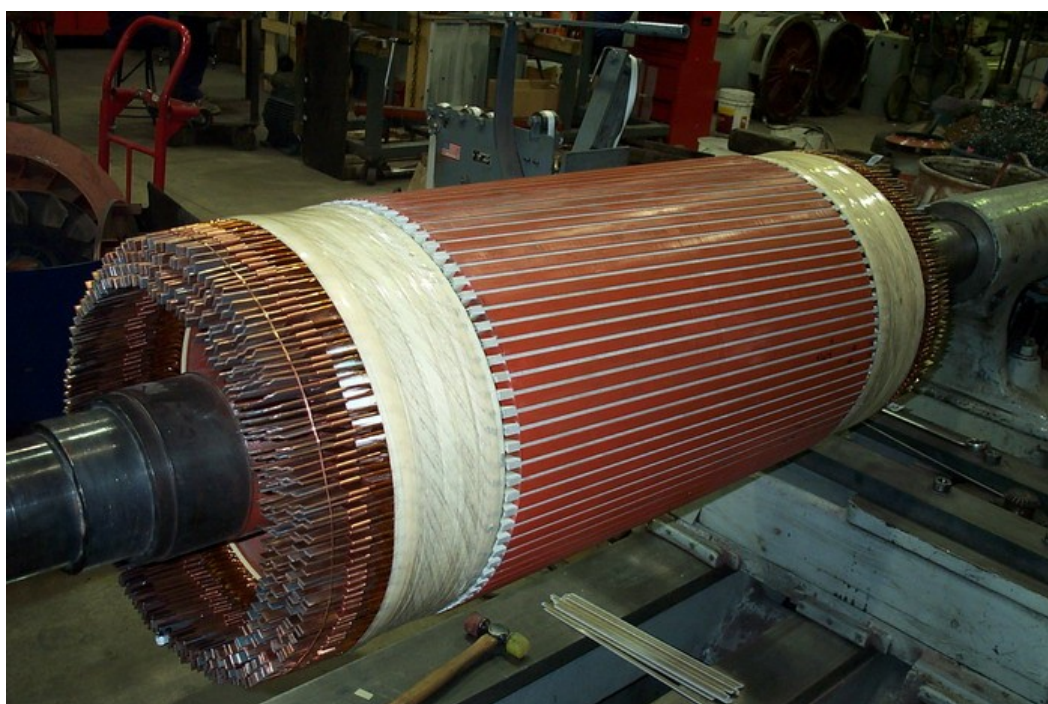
Synchronní stroj s hladkým rotorem [8]
